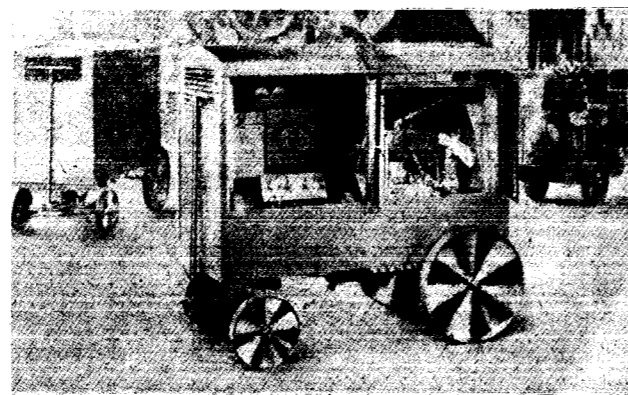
Grupo de soldadura accionado por motor de gasolina, protegido contra la lluvia.
